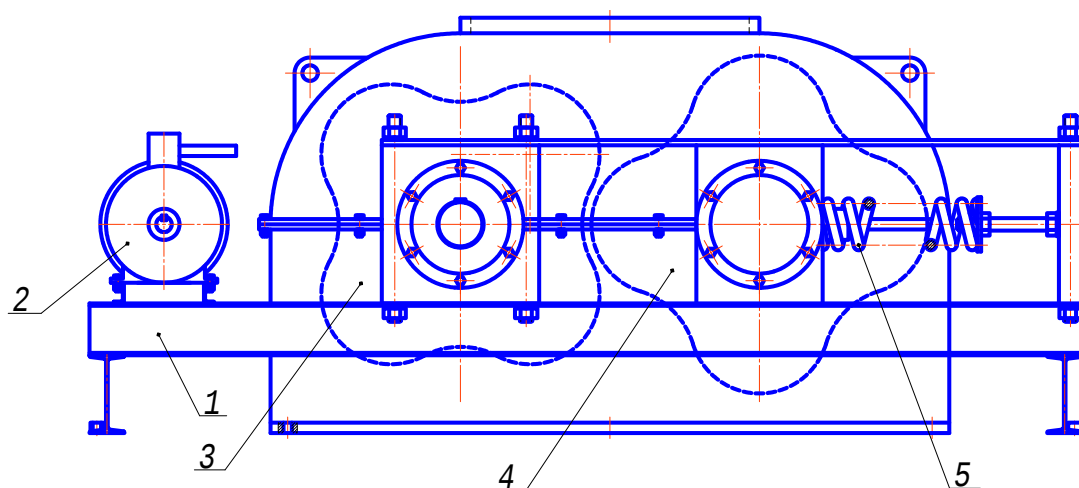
Схема валковой дробилки с выпукло-вогнутой формой валков: 1 – рама; 2 – электропривод; 3, 4 – выпукло-вогнутые валки; 5 – предохранительные пружины
